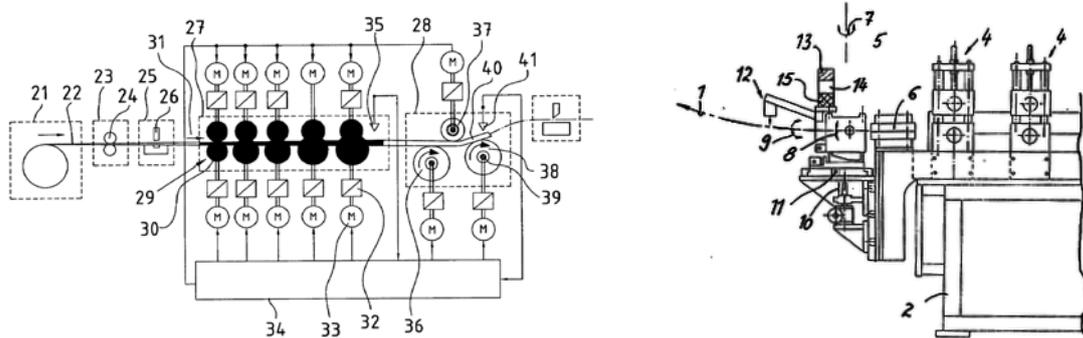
Verfahrensprinzip aus Walzprofilieren und Walzrunden nach EGIDI [100] (rechts), Verfahrensprinzip zum flexiblen Biegen von Profilen nach GÖHR [101] (links)
